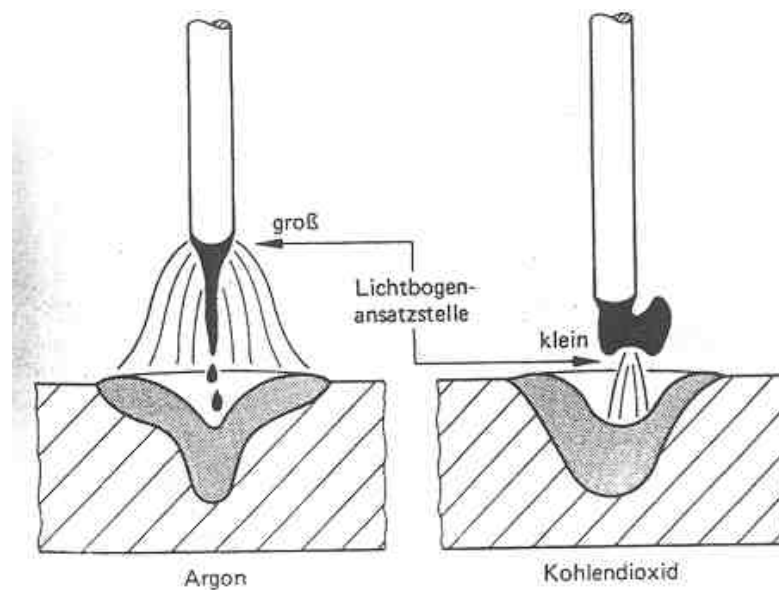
Transferência metálica por pulverização com ponta do arame inserido no arco para elevada tensão e gás de proteção Ar.
